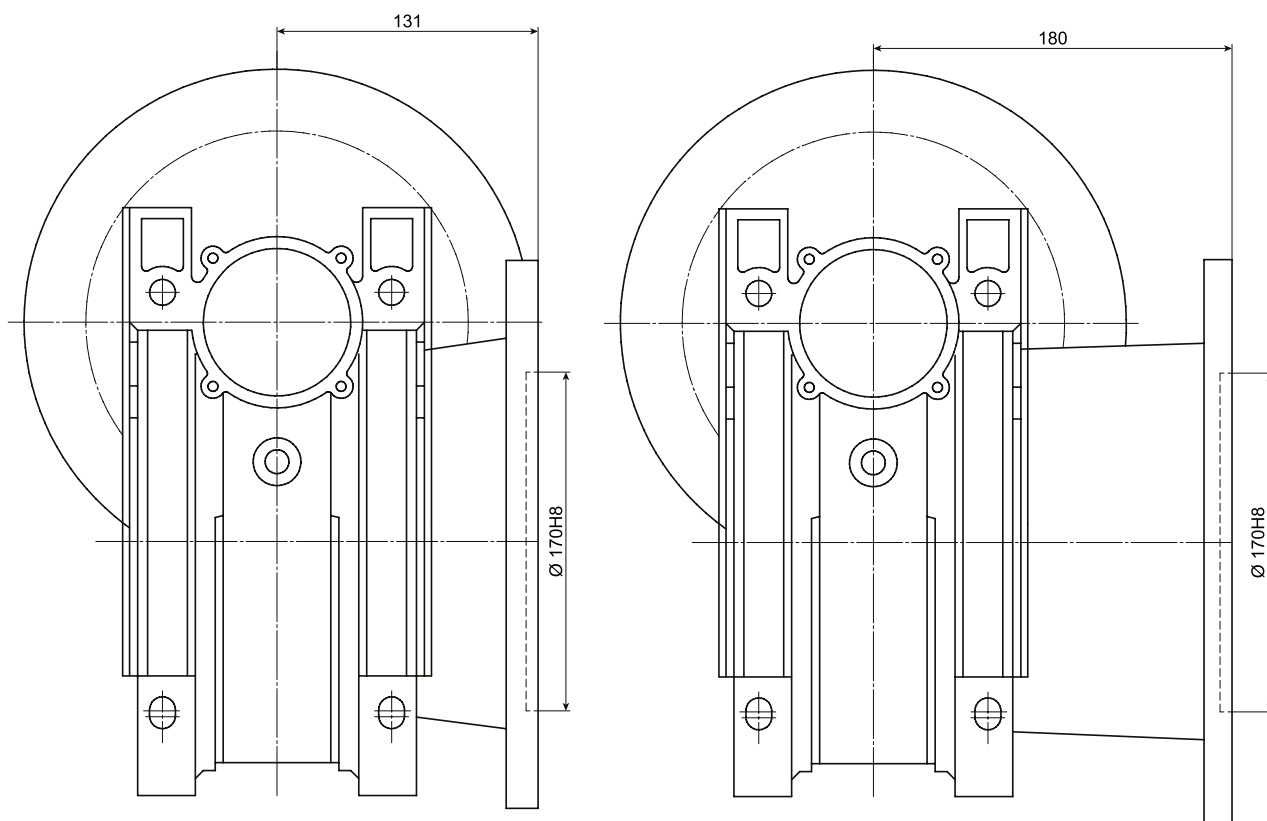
Габаритные размеры боковых фланцев FA и FB
